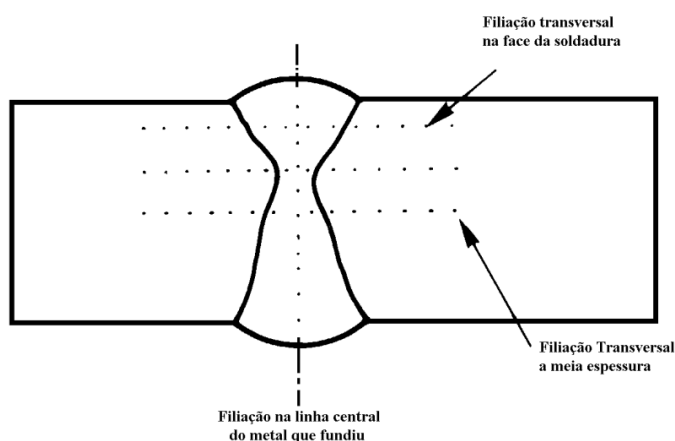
Filiações de dureza em juntas soldadas
